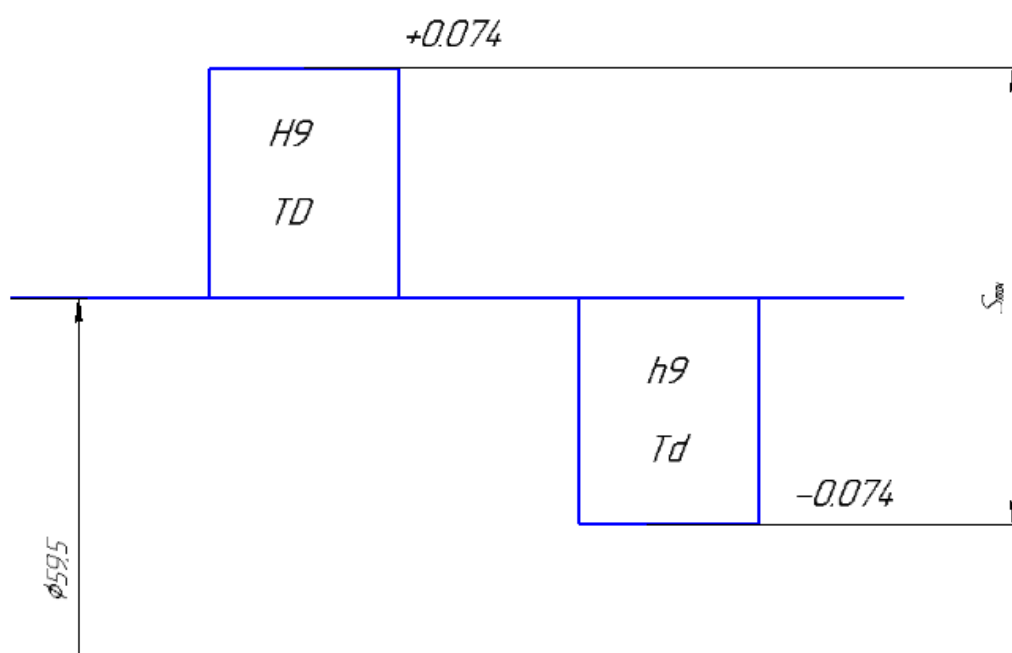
Зоны допусков оправки (Td) и заготовки (TD)
